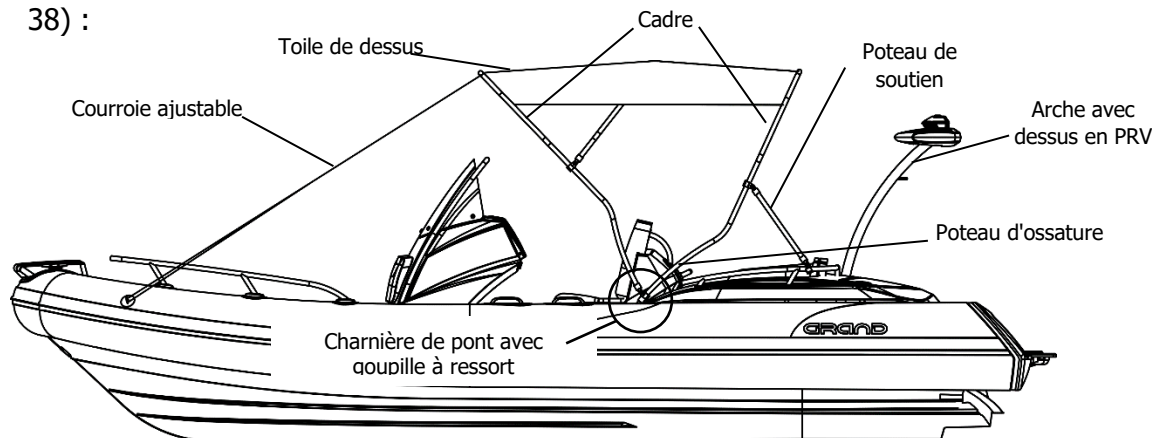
Installation du Bimini Top avec les poteaux de support sur un bateau avec une arche et un toit en PRV.
